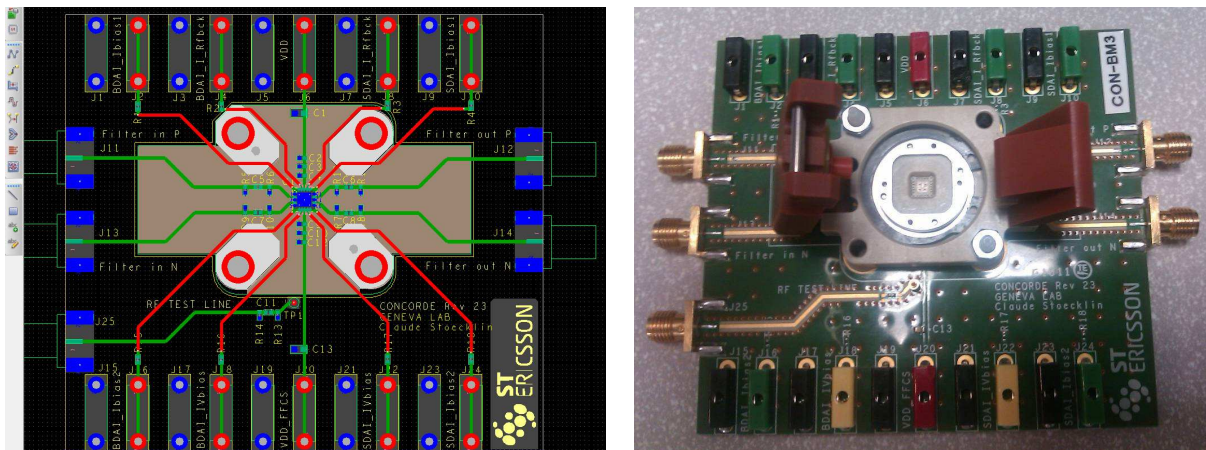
Carte de test avec « socket » pour la mesure du filtre en package QFN 4x4mm
